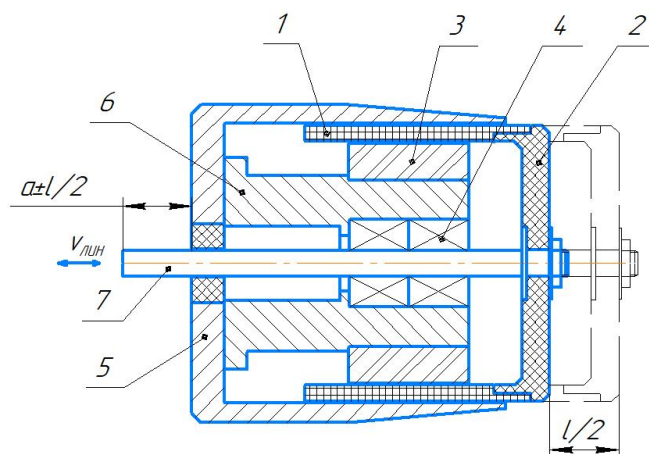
Линейный двигатель постоянного тока с полым якорем: 1 – катушка полового якоря; 2 – основание катушки; 3 – постоянный магнит; 4 – шарикоподшипники линейного типа; 5 – наружный магнитопровод; 6 – внутренний магнитопровод; 7 – рабочий шток
